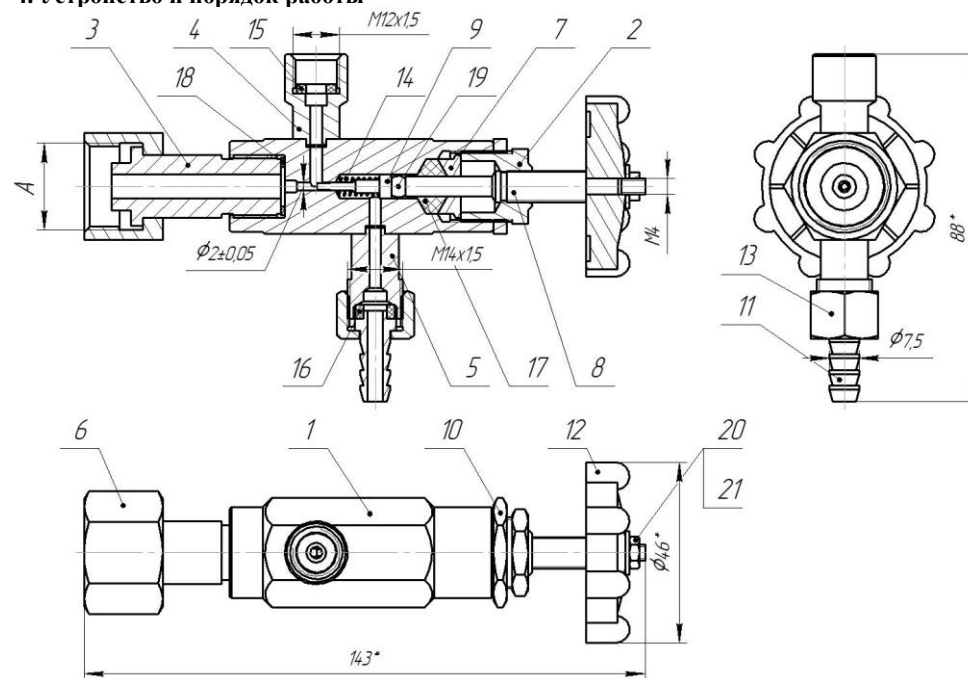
Вентиль точной регулировки ВТР-1-М160 1 – корпус; 2 – гайка; 3 – штуцер присоединительный; 4 – штуцер манометра; 5 – штуцер шланговой надставки; 6 – гайка накидная; 7 – бокс; 8 – шток; 9 – золотник; 10 – гайка поджимная; 11 – шланговая надставка (ёрш); 12 – вороток; 13 – гайка надставки поджимная; 14 – пружина возвратная; 15 – уплотнение манометра; 16 – уплотнение шланговой надставки; 17 – сальник; 18 – уплотнение штуцера; 19 – шарик штока; 20 – шайба; 21 – гайка.
